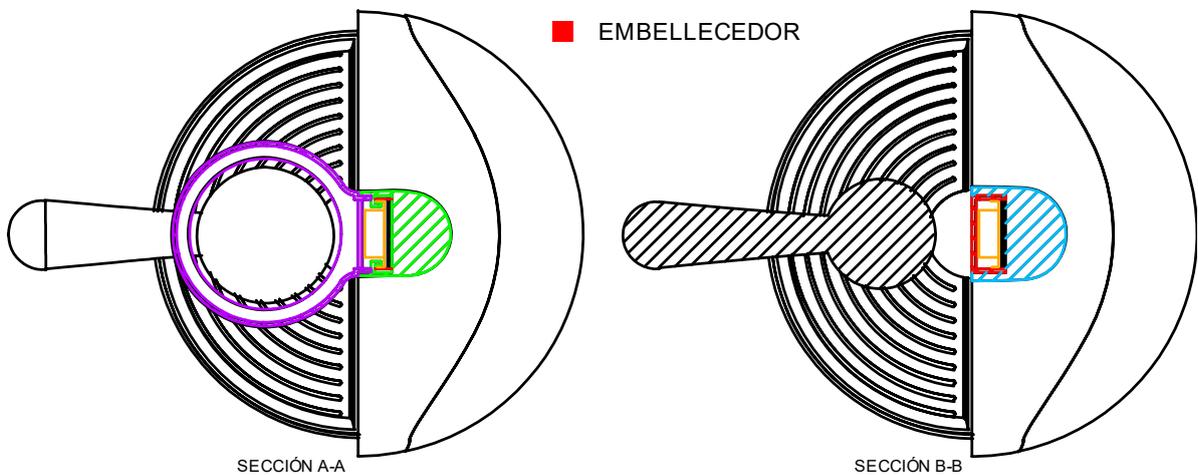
Vista de sección. Zona del sistema ranurado vs zona embellecedor
